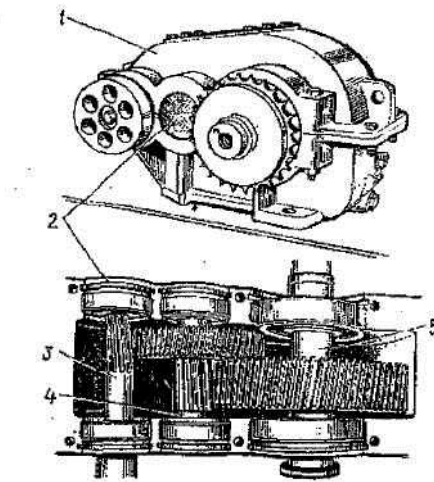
Двухступенчатый горизонтальный редуктор с цилиндрическими колесами
